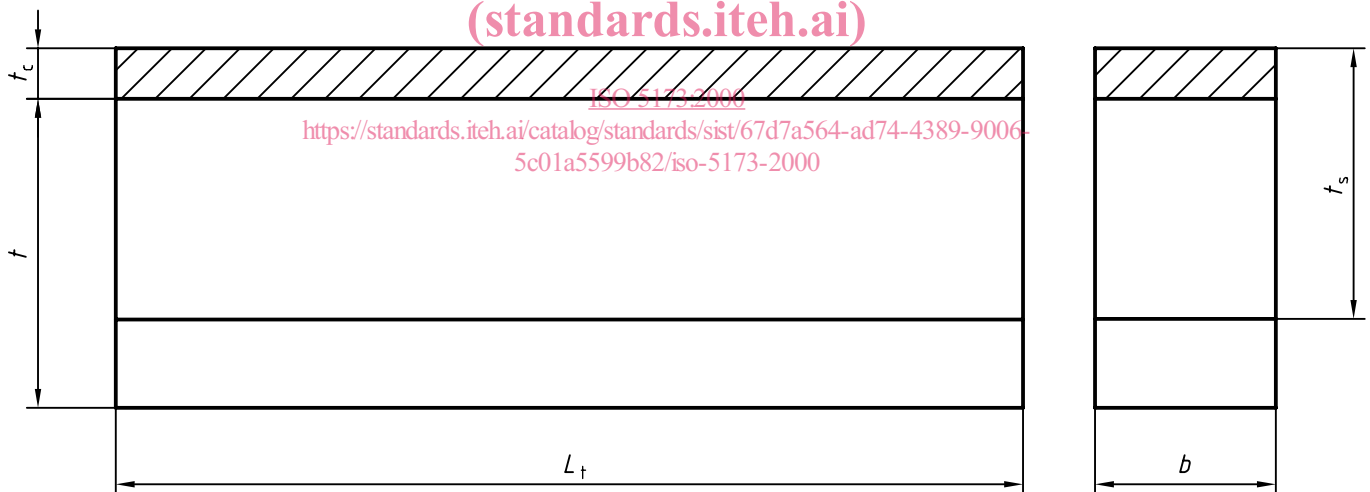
Éprouvette de pliage droit sur revêtement sans soudure bout à bout (FBC)
